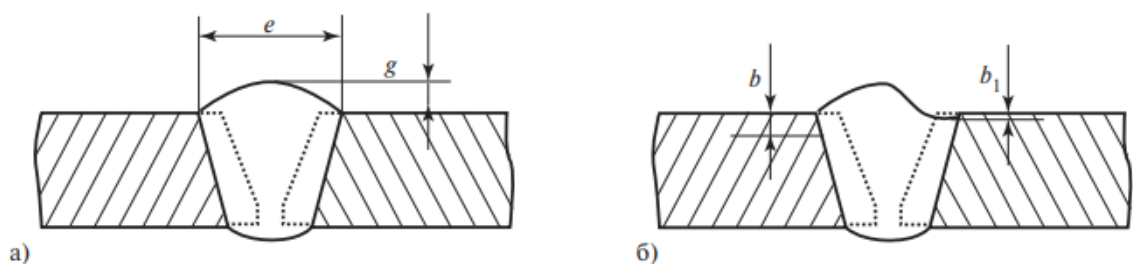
Размеры кольцевого шва сварного соединения, подлежащие измерительному контролю: а) размеры шва сварного соединения:  $e$  – ширина;  $g$  – высота; б) дефекты шва сварного соединения:  $b$  – глубина несплавления, выходящего на поверхность;  $b_1$  – глубина подреза
